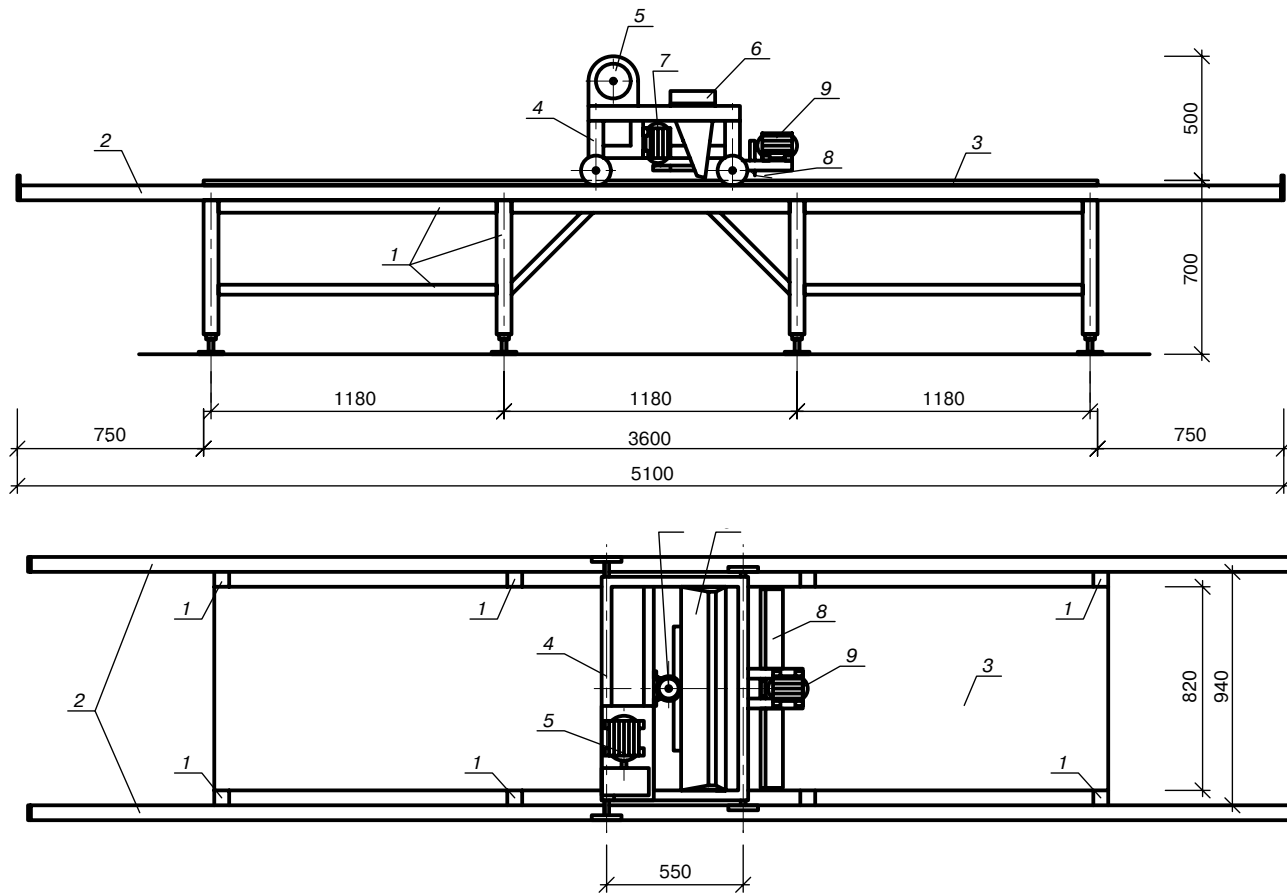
Формовочная установка: 1 – несущая рама формовочной установки; 2 – направляющие каретки; 3 – рабочий поддон; 4 – передвижная каретка с установленным оборудованием; 5 – привод передвижения каретки с регулировкой скорости перемещения; 6 – съемный бункер для смеси; 7 – вибропривод бункера; 8 – заглаживающее устройство; 9 – вибропривод заглаживающего устройства
